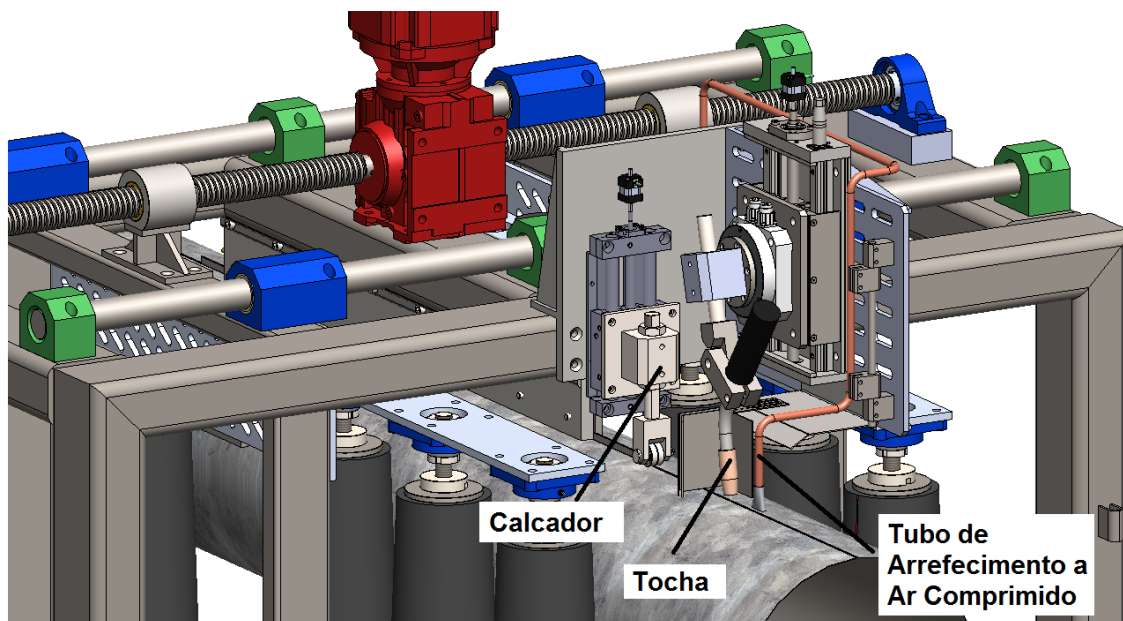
Mecanismos de arraste, posicionador da tocha e tubo de arrefecimento
